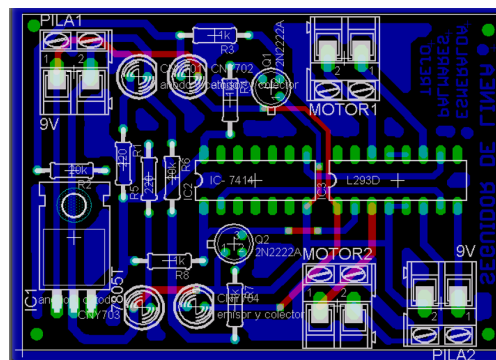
Diseño final de la tarjeta PCB de control del seguidor de línea.
